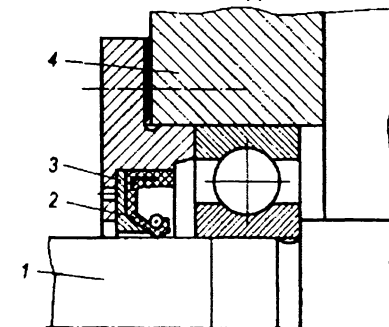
Манжета с опорным конусом при повышении давления ($>0,05$ МПа) внутри корпуса: 1 – вал; 2 – манжета; 3 – опорный конус; 4 – корпус
